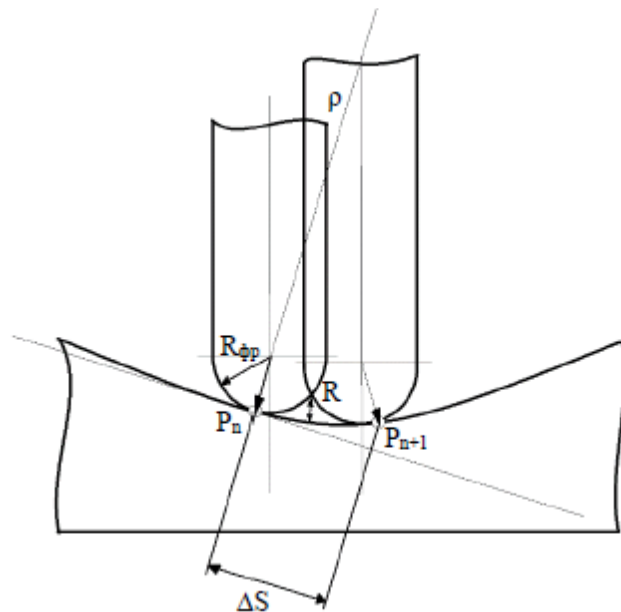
Схема формування ребристості при фрезеруванні формотворчої поверхні
